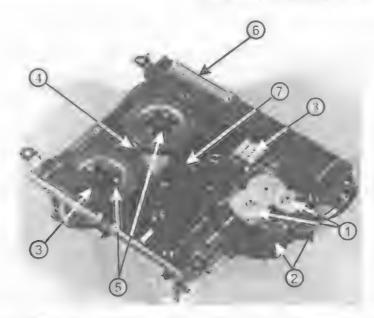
1— шестерни привода микролифта; 2— электромоторы; 3— шасси ЛПМ; 4— пассик; 5— маховики; 6— соединитель; 7— плата управления механизма реверса; 8— шлейф
